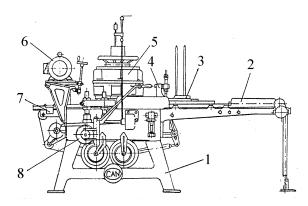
Машина для предварительной закатки банок 6-C: 1 — станина; 2 — загрузочное устройство; 3 — механизм подачи крышек; 4 — механизм маркировки крышки; 5 — закаточная карусель; 6 — привод; 7 — разгрузочное устройство; 8 — муфта включения
